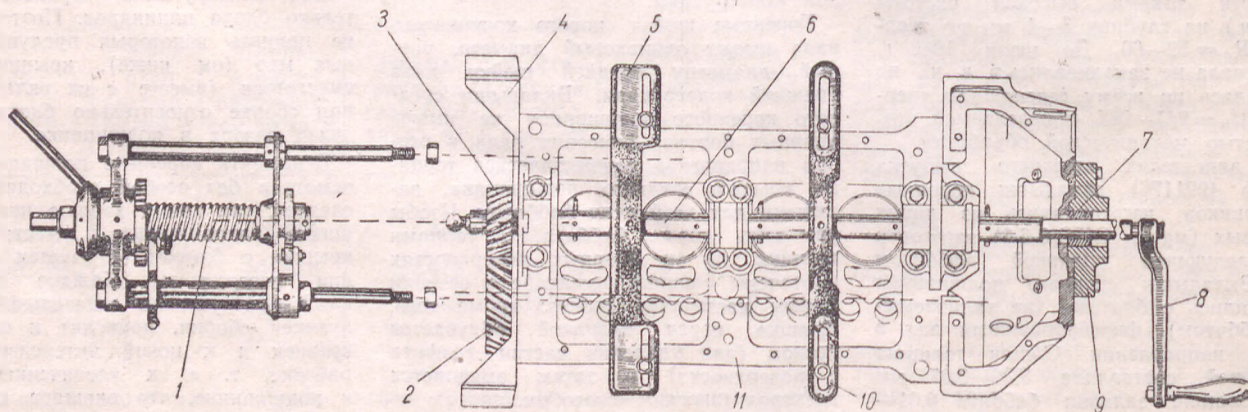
Приспособление для расточки вкладышей коренных подшипников двигателя.
